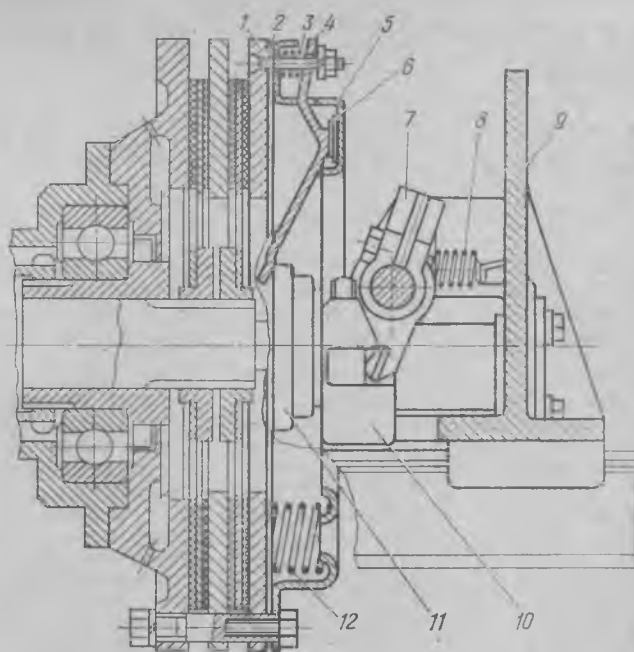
Фрикционная муфта (серийная): 1 — прижимной диск сцепления; 2 — винт, включающий сцепление; 3 — пружина выключающего винта; 4 — выжимное коромысло (сцепление); 5 — крышка сцепления; 6 — натяжная пружина коромысла; 7 — вилка сцепления; 8 — пружина; 9 — механизм отключения муфты; 10 — муфта выключения вентилятора; 11 — нажимной шарикоподшипник; 12 — включающая пружина
